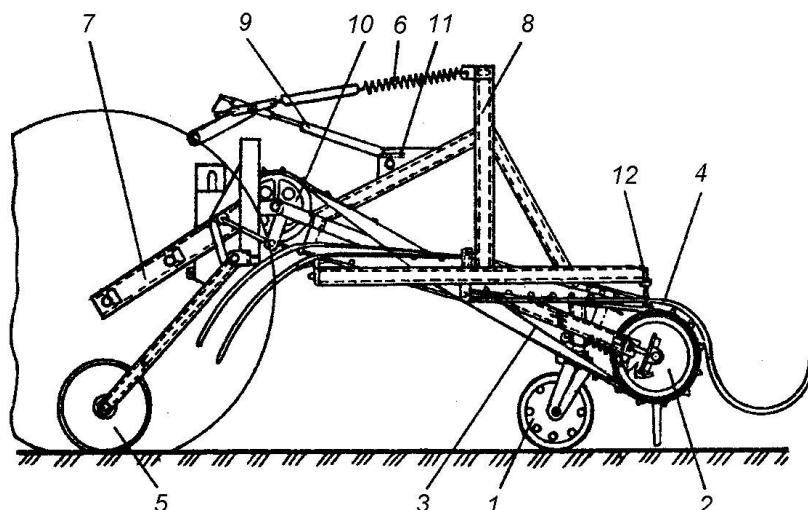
Схема оборачивателя лент льна ОЧН-1: 1 – копирующее колесо; 2 – барабан; 3 – перекрестный ремень; 4 – направляющие; 5 – прикатывающий каток; 6 – уравнивающая пружина; 7 – рама навески; 8 – основная рама; 9 – тяга; 10 – привод; 11 – кронштейн; 12 – регулировочный винт
